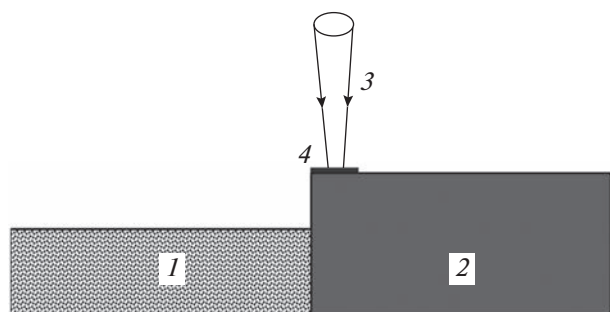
Схема сварки разнотолщинных пластин: 1 – пористая пластина; 2 – монолитная (непористая) пластина; 3 – луч лазера; 4 – слой наносодеждающей композиции.
